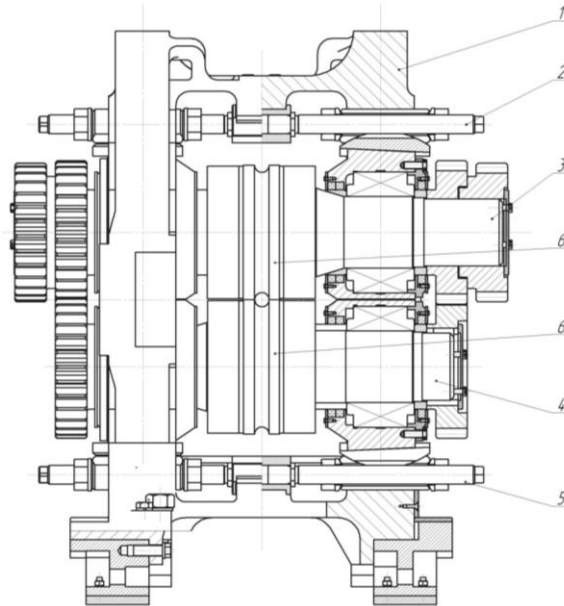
Робоча кліть стану ХПТ: 1 – станина, 2 – верхній натискний пристрій, 3 – верхній робочий валок, 4 – нижній робочий валок, 5 – нижній натискний пристрій, 6 – калібр робочого валка.
